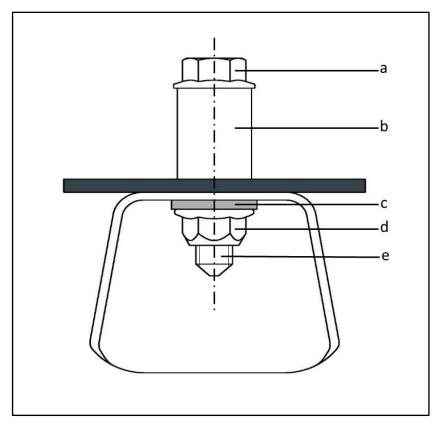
Exemple d'assemblage vissé protégé contre le desserrage (schéma de principe)
